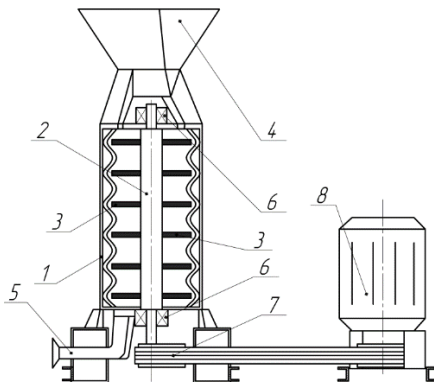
Конструктивная схема роторно-вихревой мельницы: 1- стенки корпуса со съемной футеровкой; 2 – ротор; 3 - била; 4 - загрузочное отверстие; 5 – разгрузочное отверстие 6 – подшипниковые опоры; 7 – редуктор; 8 - электродвигатель
